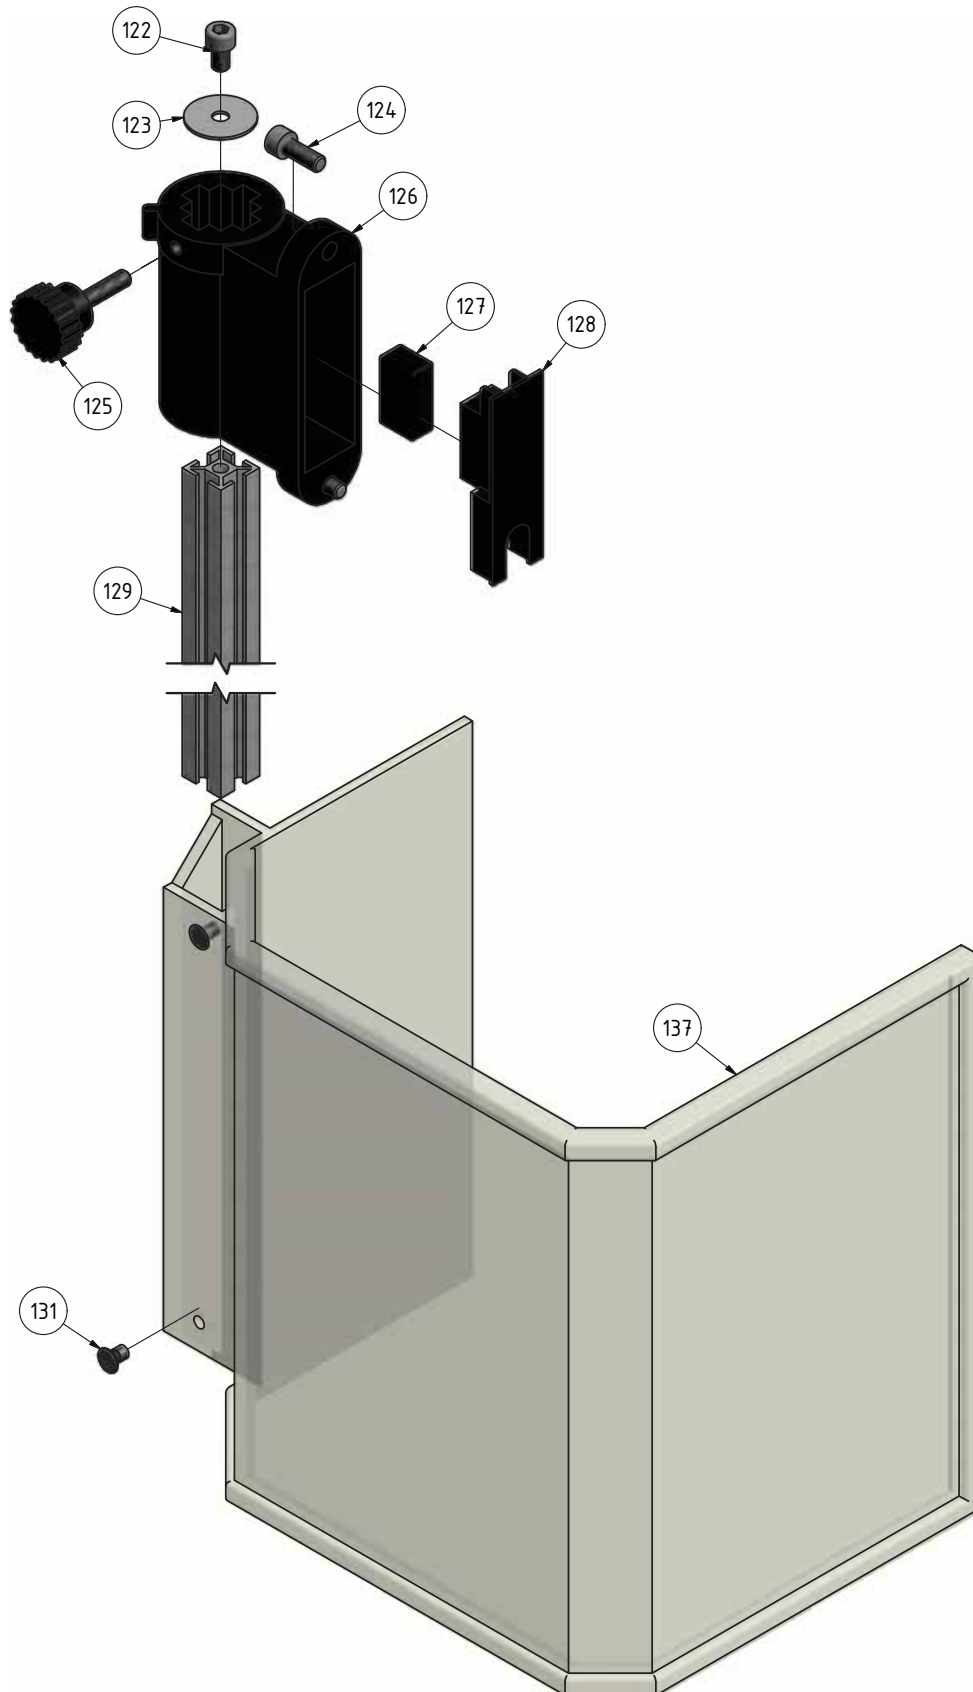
Bohrfutterschutz - Drilling chuck protection
